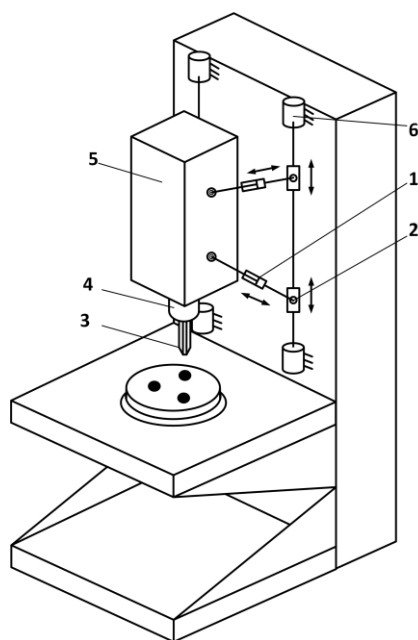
Гибридная компоновка вертикального резьбонарезного станка с комбинированными МПС
